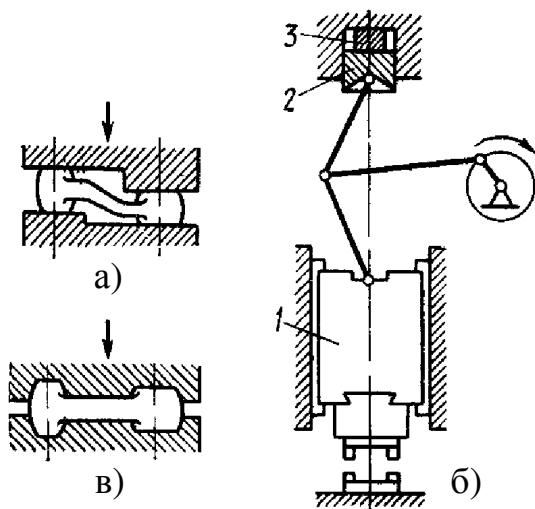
Схеми калібрування і кривошипно-колінного преса
